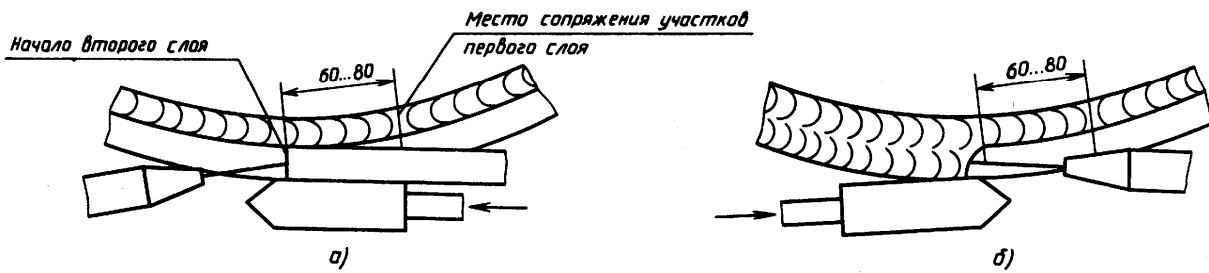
Схема начала процесса сварки второго слоя
